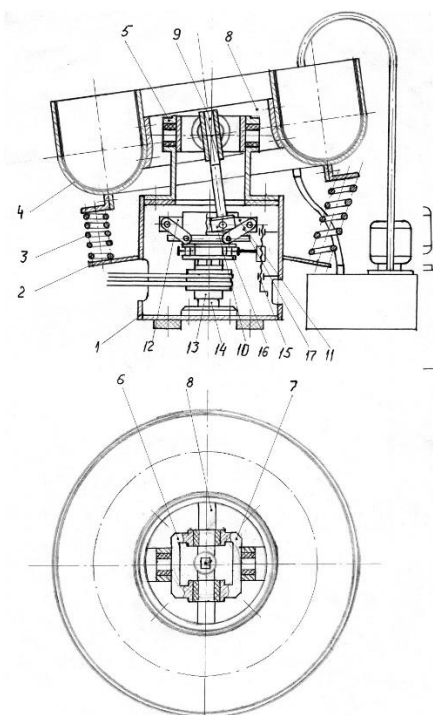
Конструктивна схема вібраційно-відцентрової установки ВВУ II.
